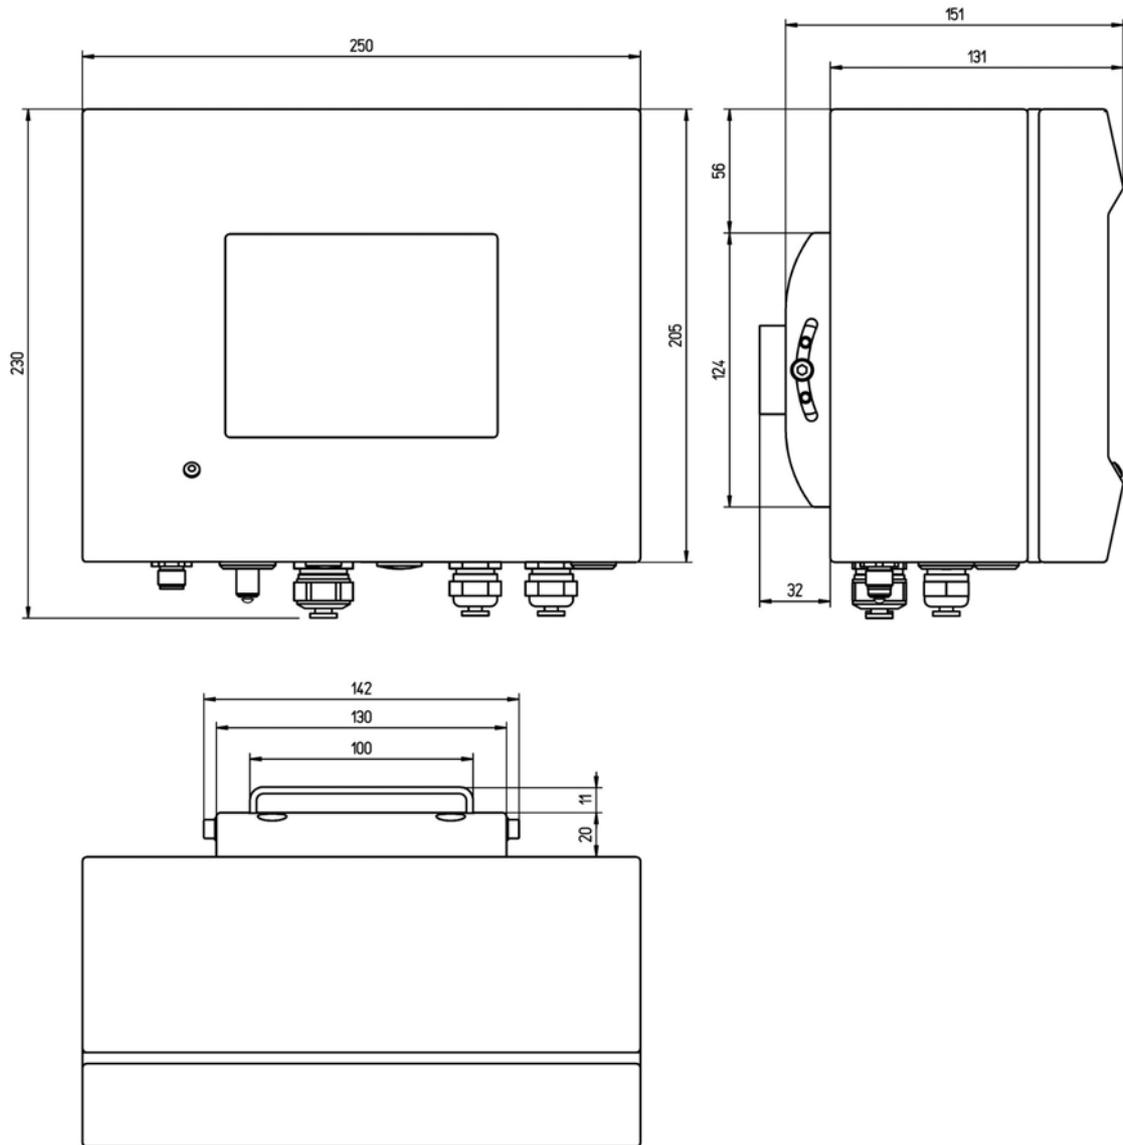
Dimensiones (mm) del instrumento: montaje en pared y en tubería
